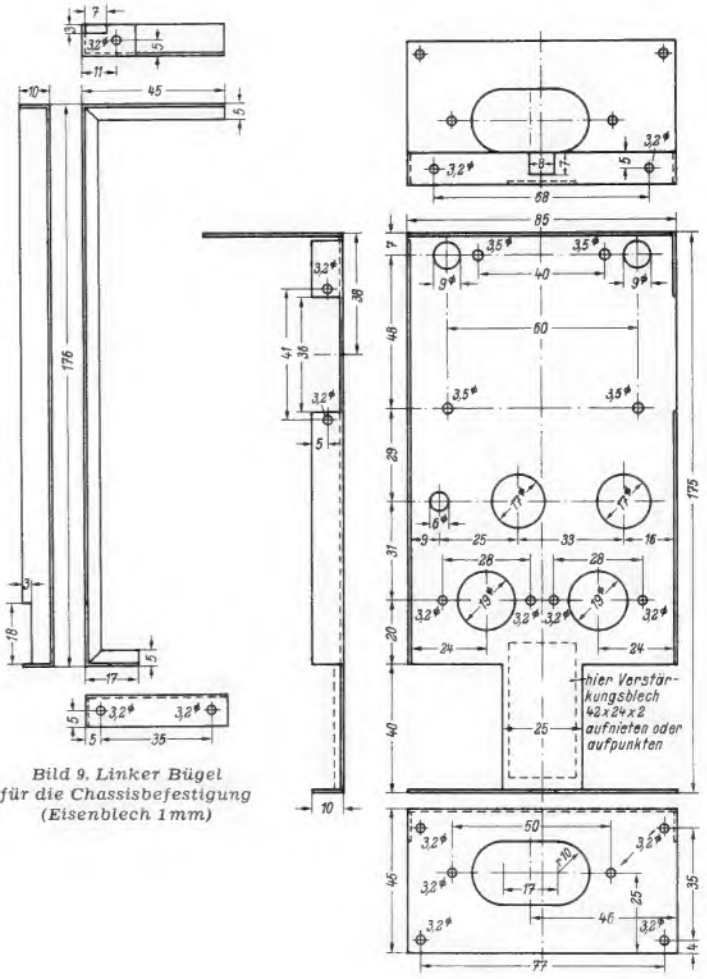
Chassis mit Bohrungen; Material: Eisenblech 1mm
